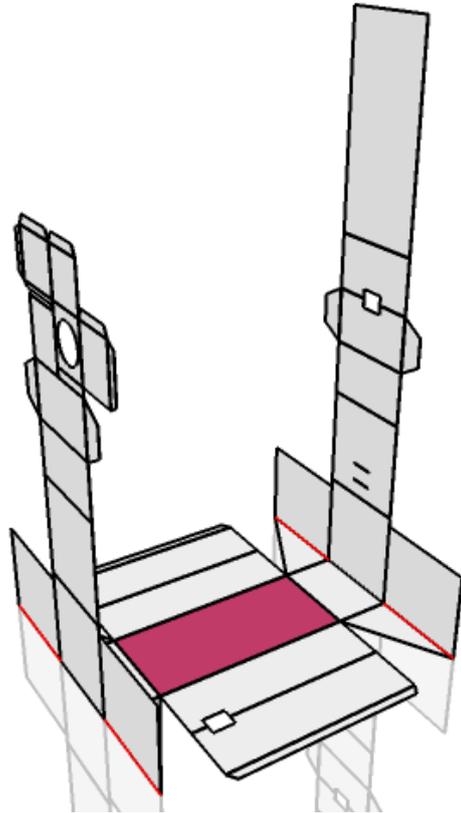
Guía de plegado. Plegado tapas 2. Fuente: Elaboración propia.
